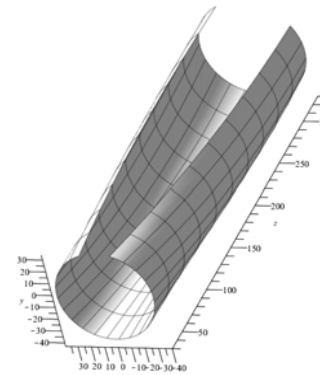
Инструментальная поверхность фрезы, обрабатывающей внутреннюю поверхность лопатки
